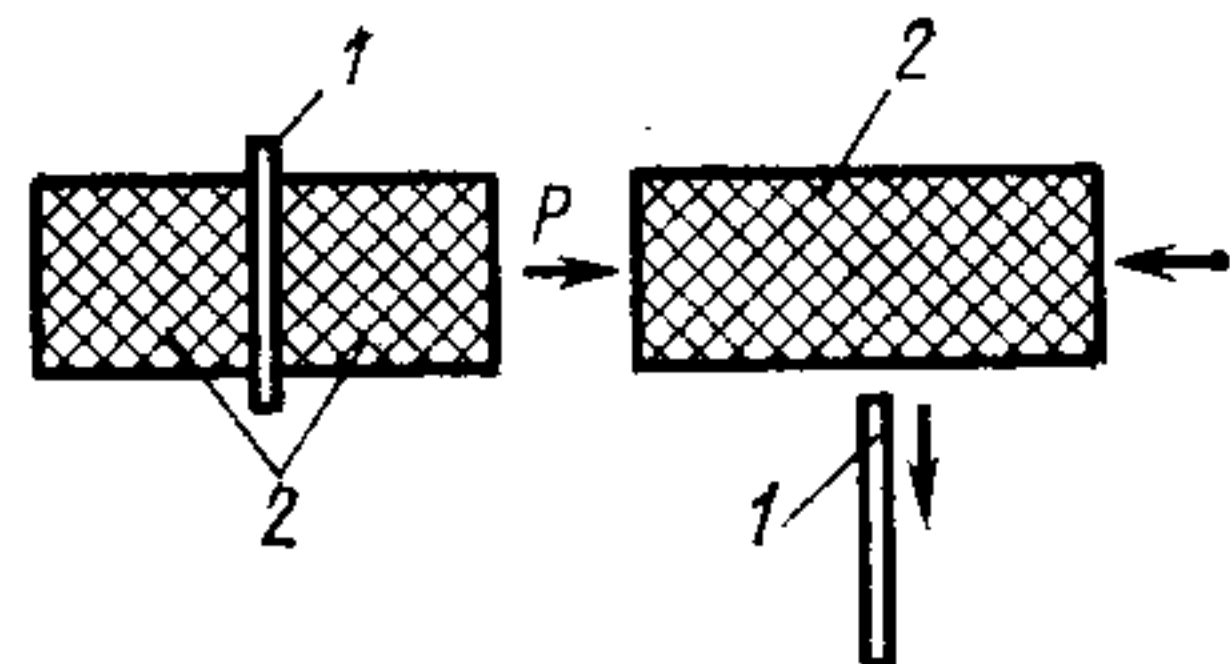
Сварка горячим «лезвием»: а — в начале сварки; б — сваренные пластмассы
